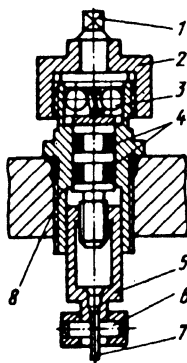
Регулировочный винт механизма 6%-ной коррекции:
